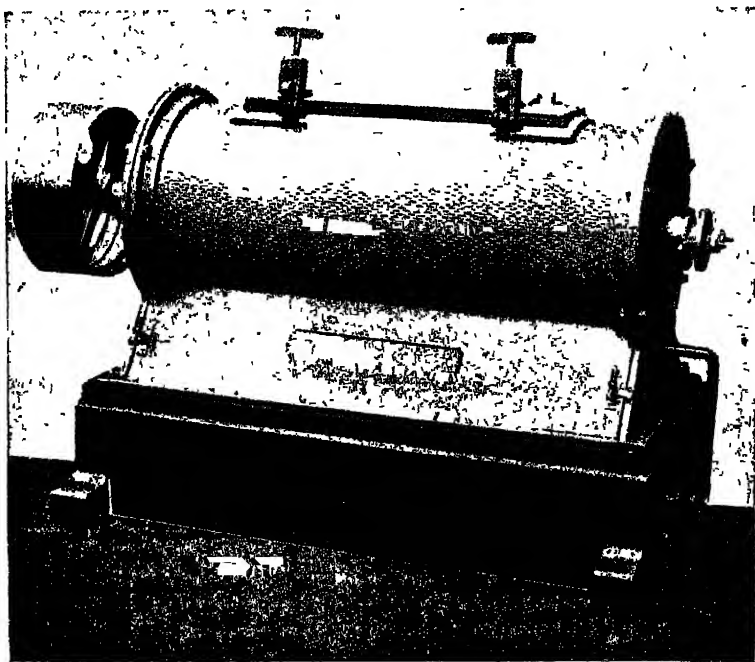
Machine à polir ou « brillanteuse » pour la fabrication de la poudre d'aluminium (d'après L. Guillet).
